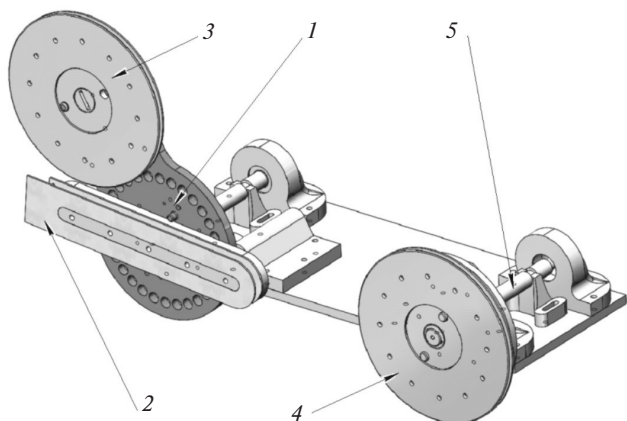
Схема намоточного устройства для изготовления ВТСП обмоток типа «двойная галета»
